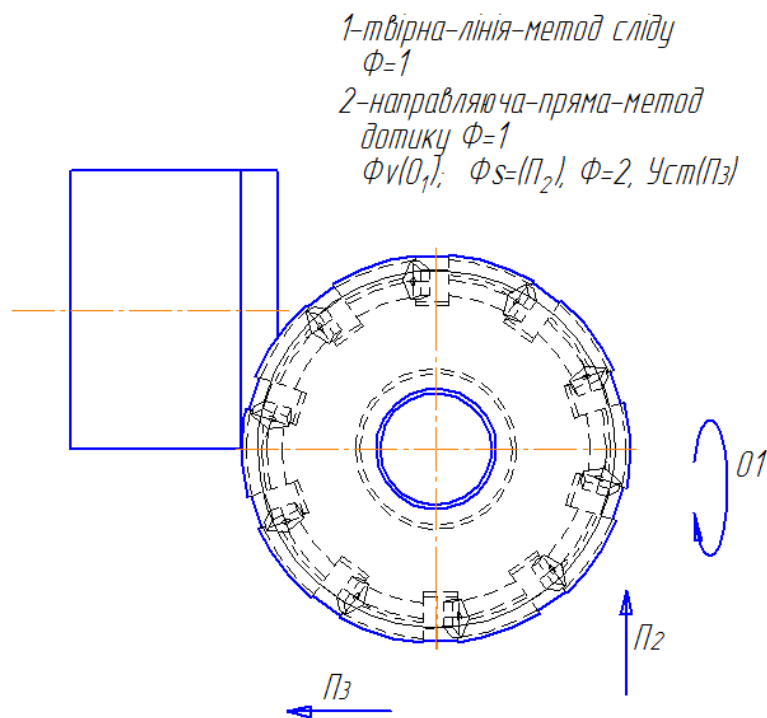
Формоутворення при фрезеруванні пазу торцевою фрезою
